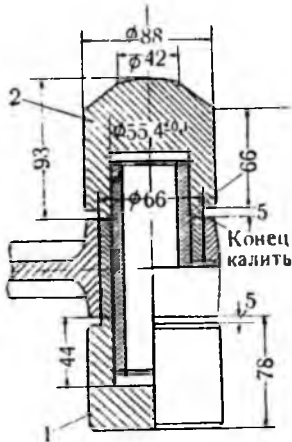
Приспособление Чернышкова для обсадки (восстановления) втулок верхних головок шатунов и др.:
